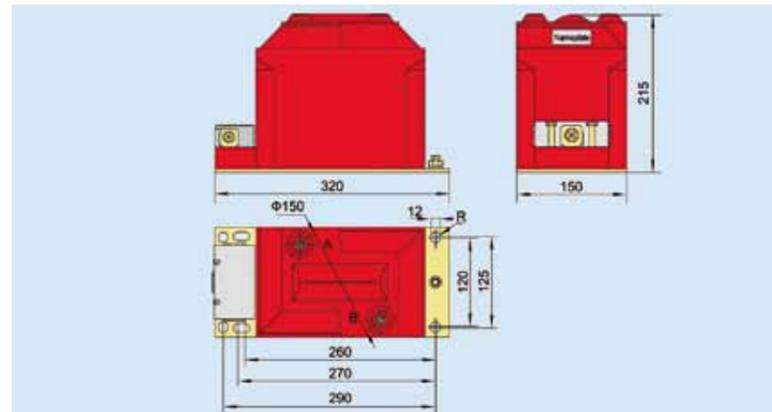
Внешний вид и монтажные размеры трансформатора напряжения JDZ10-6
